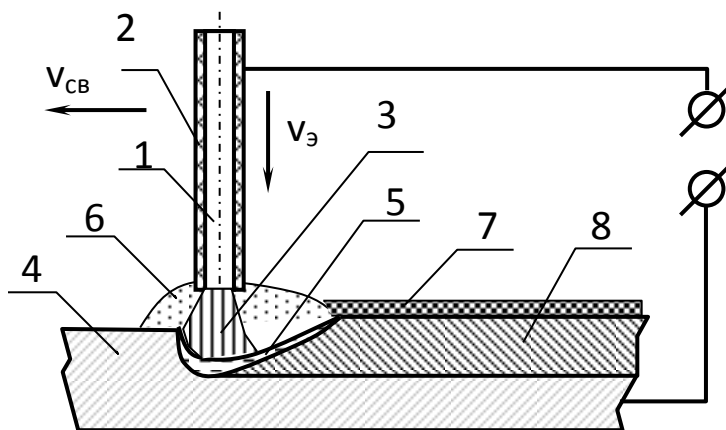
Схема ручной дуговой сварки
